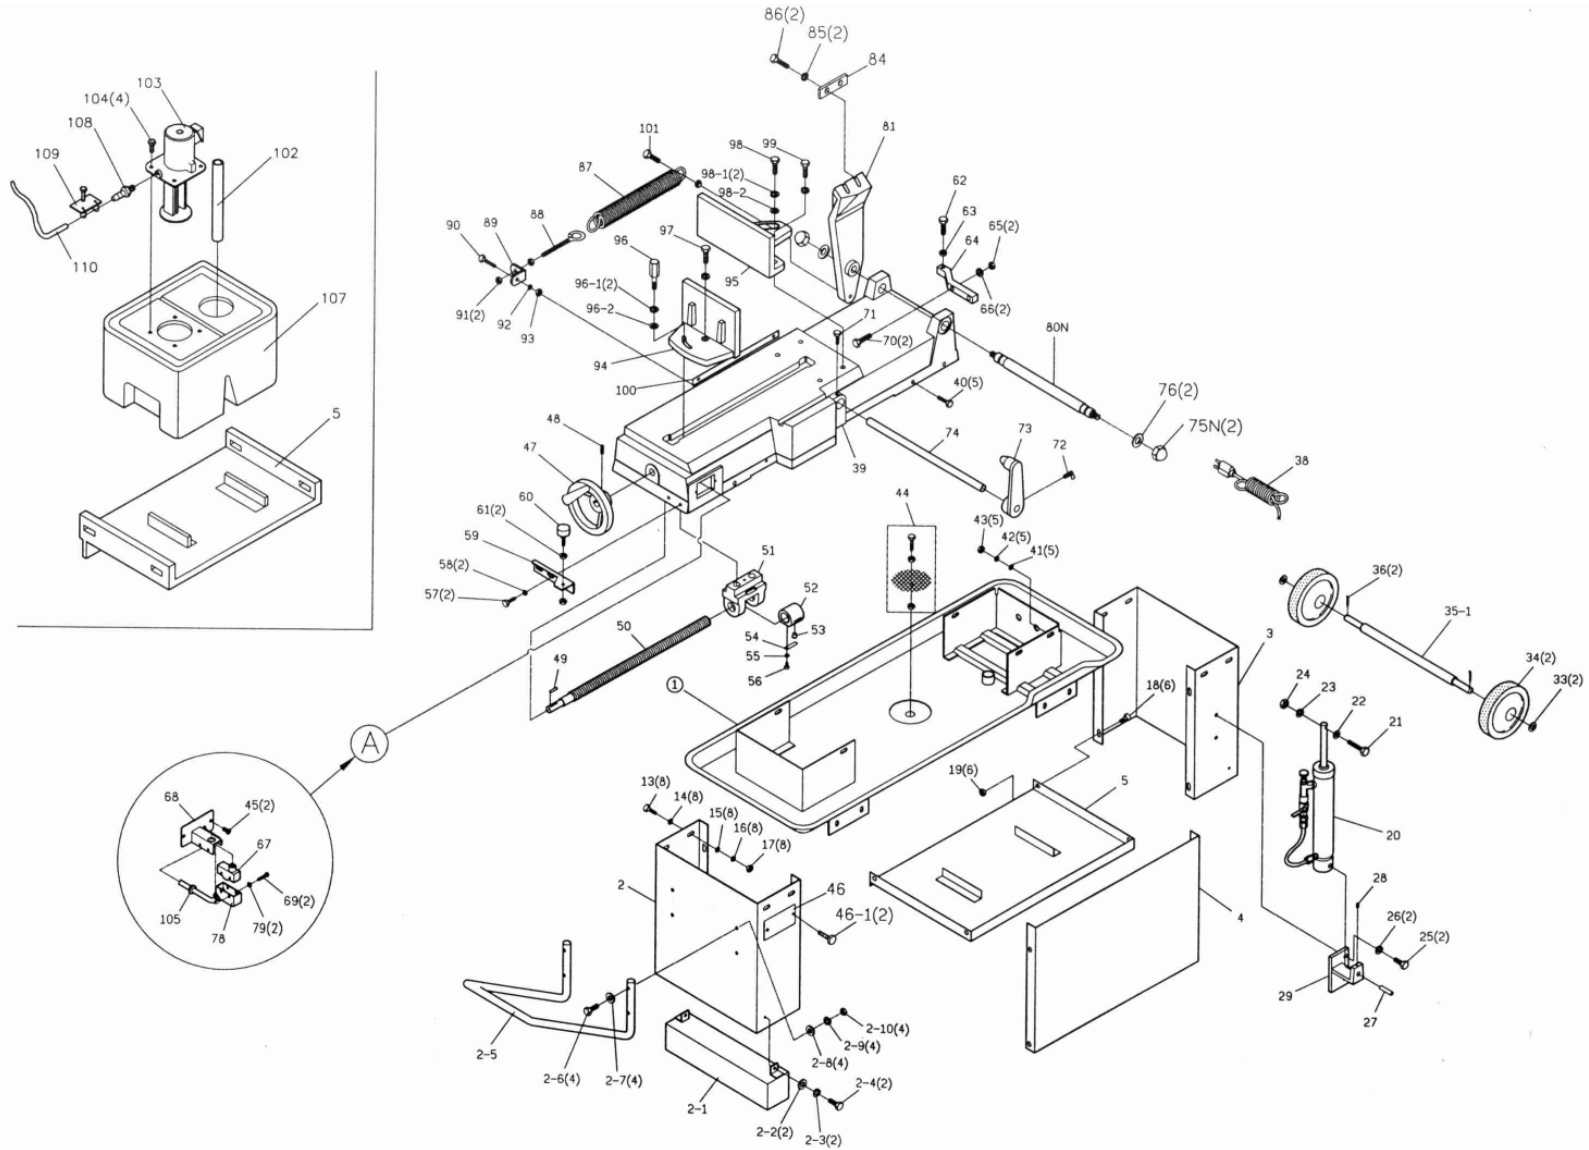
Explosionszeichnung - Explosion drawing 1
